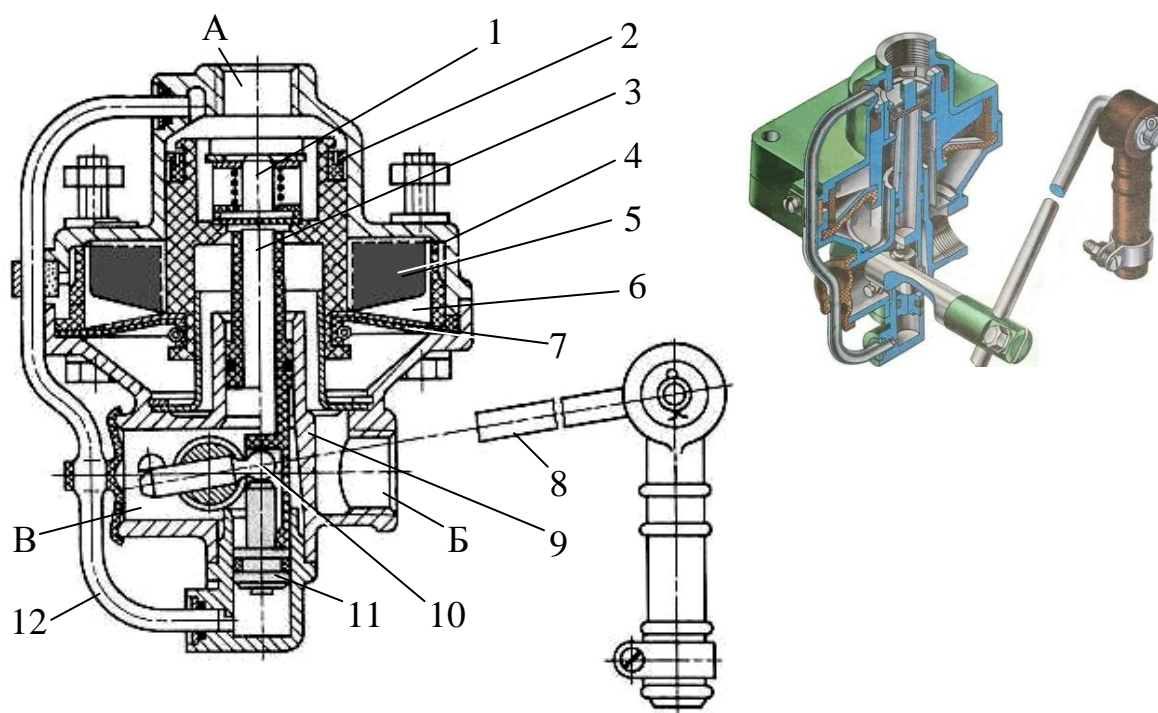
Конструкция автоматического регулятора тормозных сил грузового автомобиля-тягача КАМАЗ: 1 – клапан; 2 – ступенчатый поршень; 3 – толкатель; 4 – неподвижная вставка; 5 – ребра поршня; 6 – ребра неподвижной вставки; 7 – мембрана; 8 – рычаг; 9 – направляющая толкателя; 10 – шаровая пята; 11 – поршень; 12 – соединительная трубка; А – вывод к тормозному крану; Б – вывод к тормозным камерам колес задней тележки; В – вывод в атмосферу
